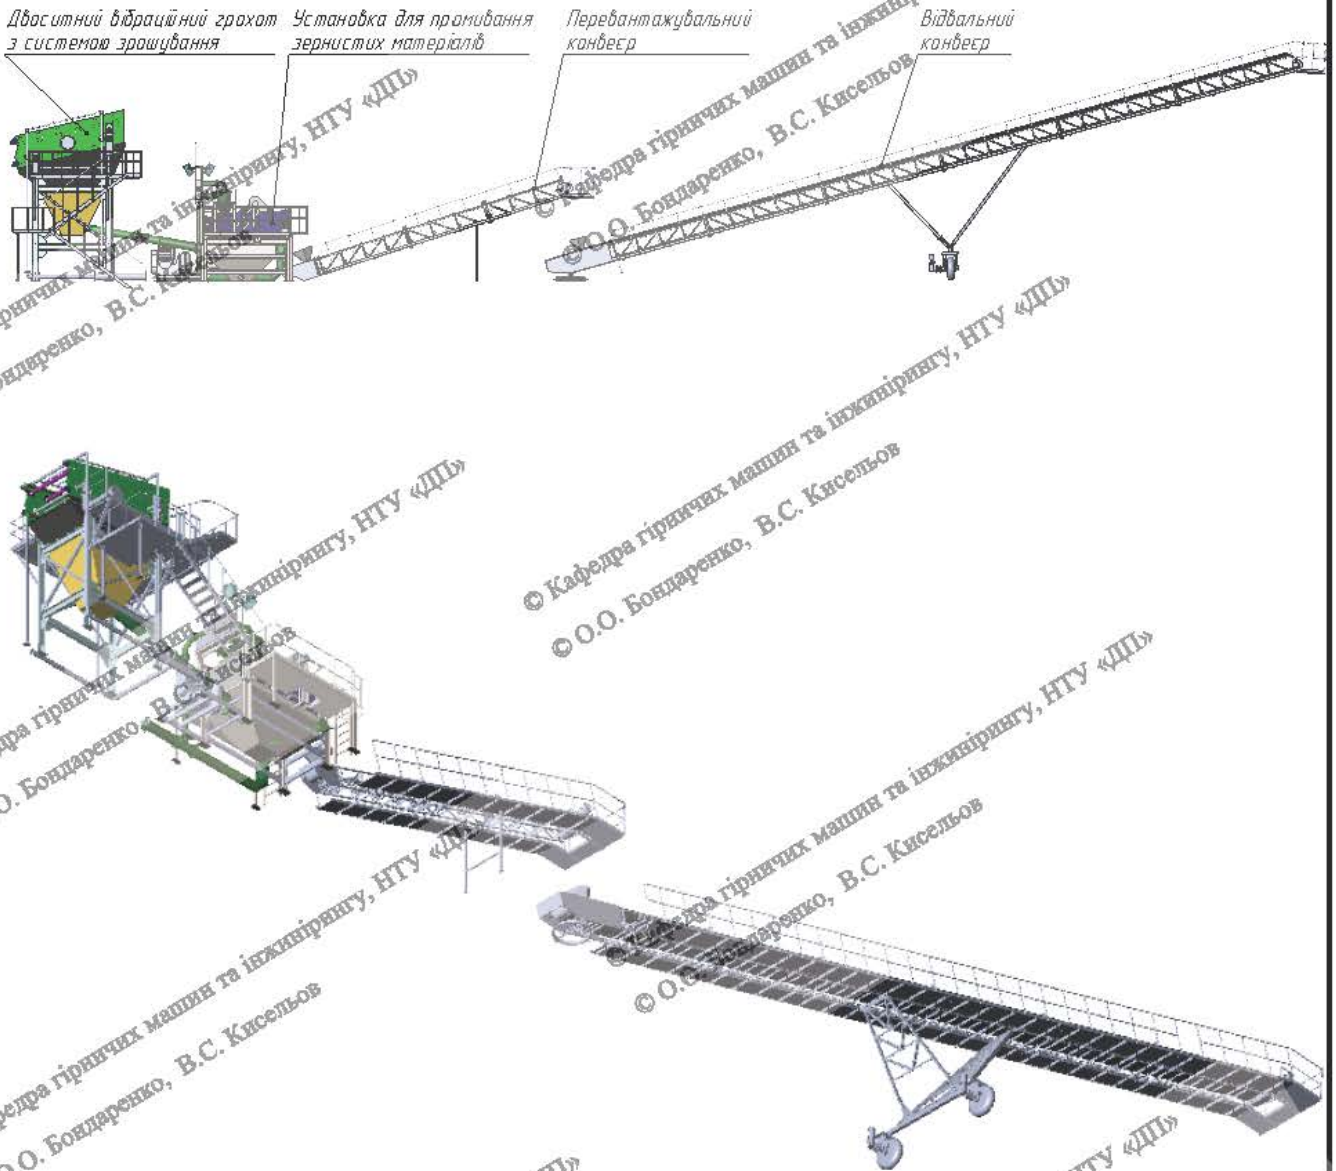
Установка для переробки зернистих матеріалів
